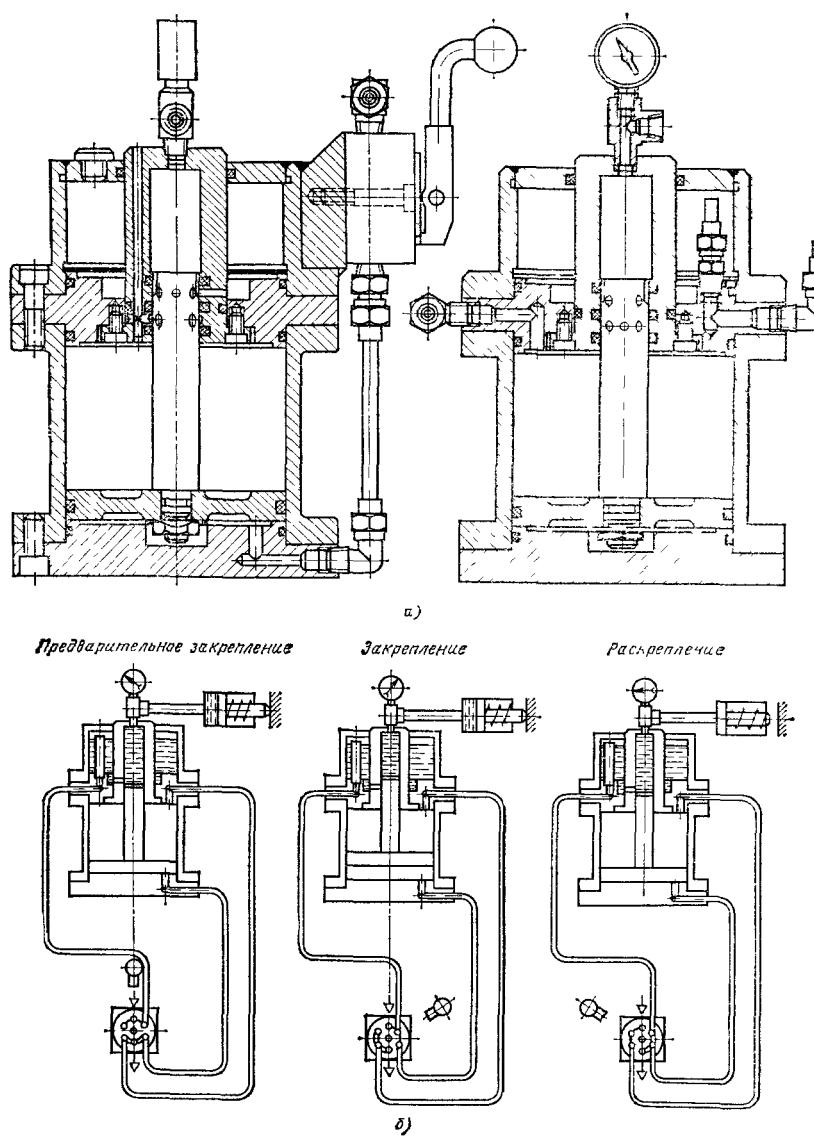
Двухступенчатый пневмогидропреобразователь мод. С7027-4007:
